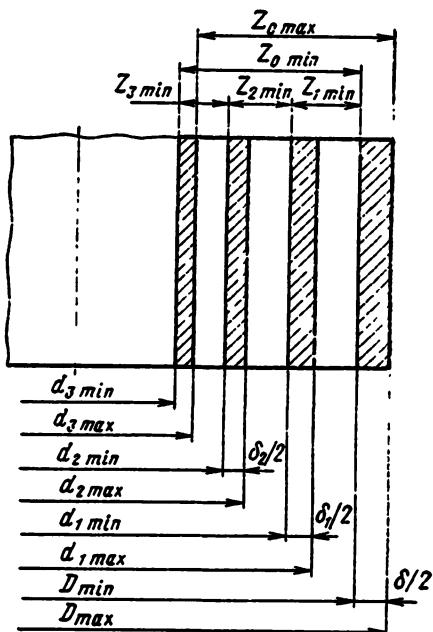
Схема расположения припусков и промежуточных размеров для вала
